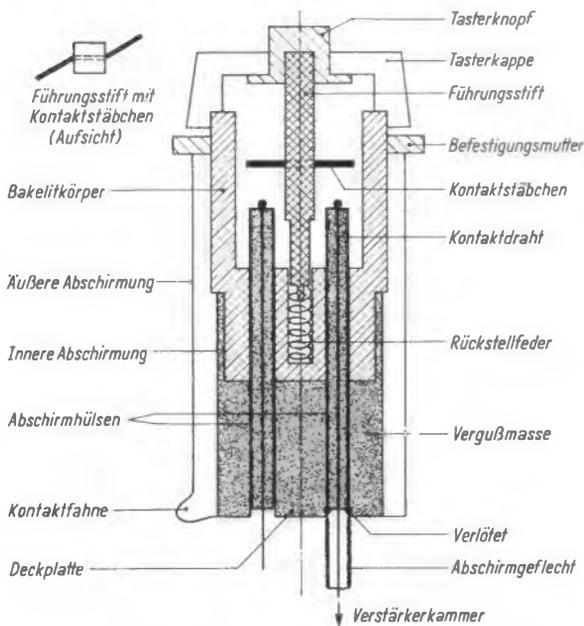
Schnittzeichnung für den umgebauten kapazitätsarmen Meßtaster
